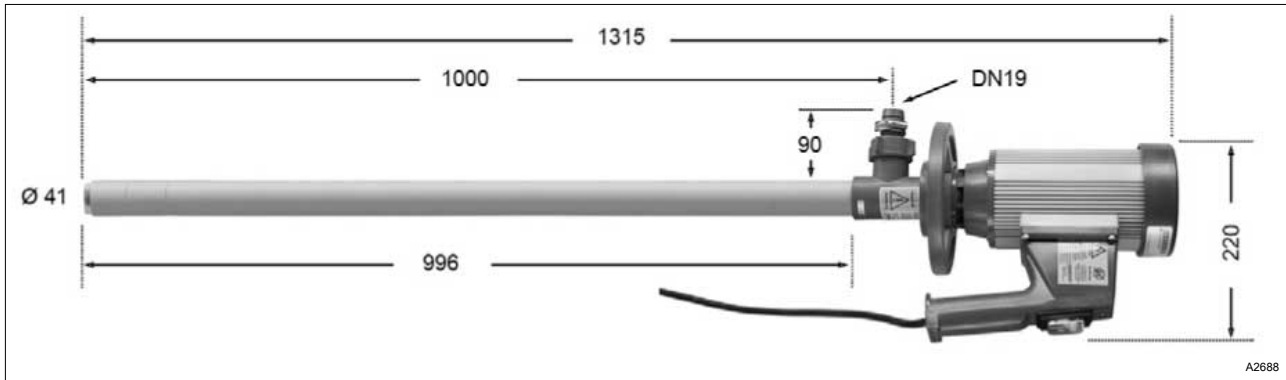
Ausführung PP: Maßzeichnung mit Hauptabmessungen, alle Angaben in mm.
